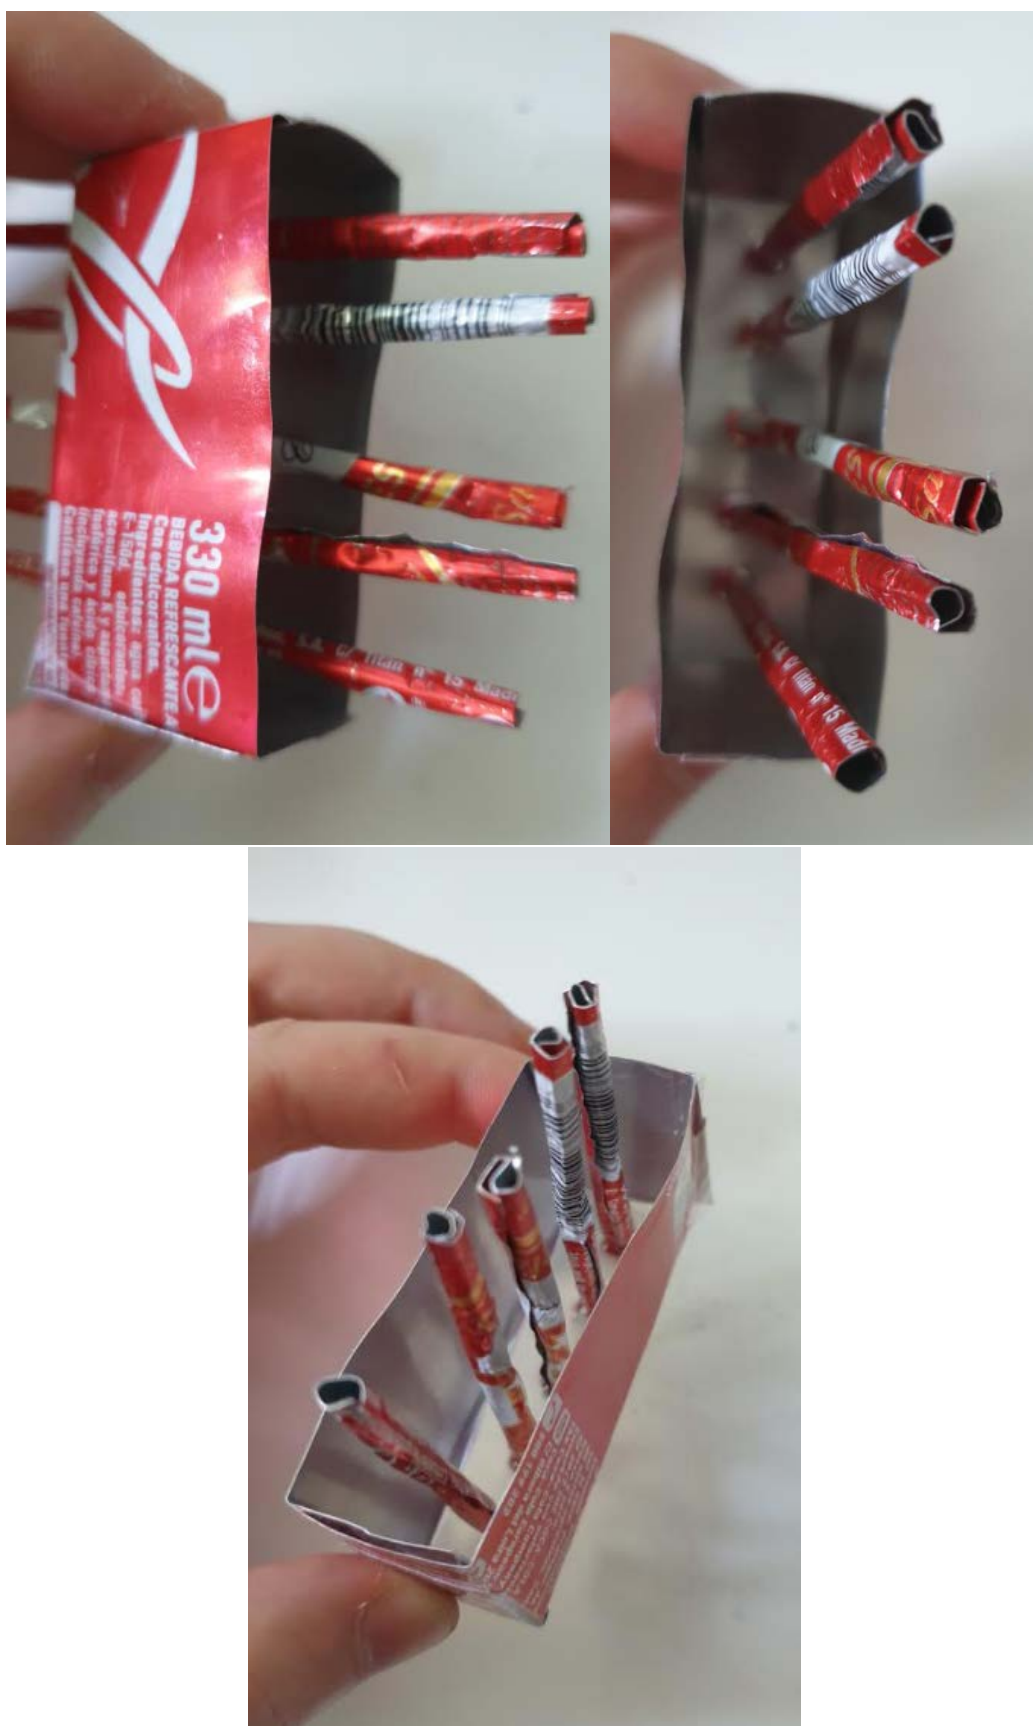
Molde del anclaje de cuerdas al brazo acabad
